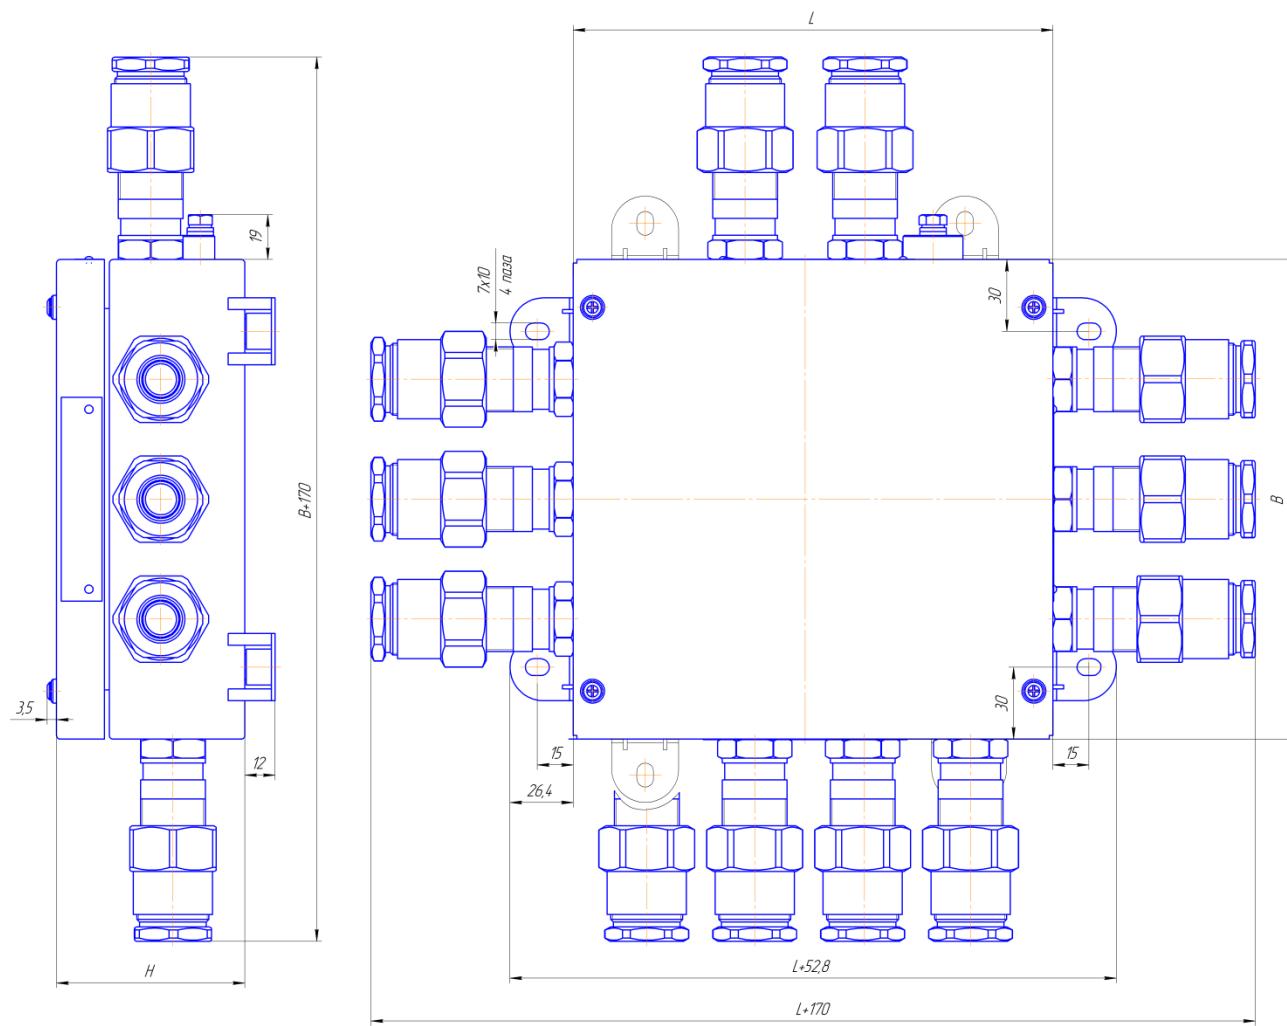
Габаритно-монтажный чертеж исполнений ККВ-е
